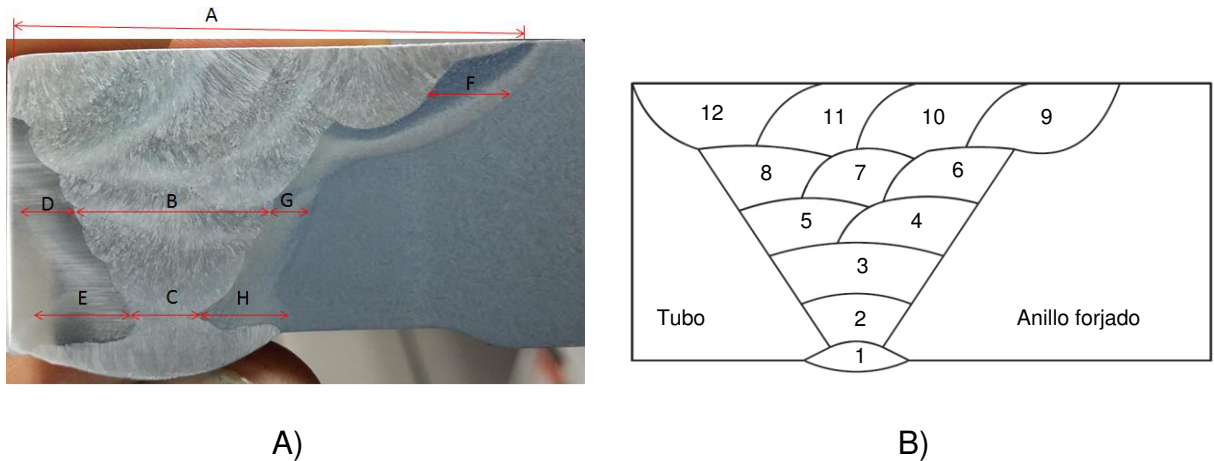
A) Macrografía de la soldadura, B) Representación esquemática de la macrografía que revela la secuencia de deposición de los cordones de soldadura.
